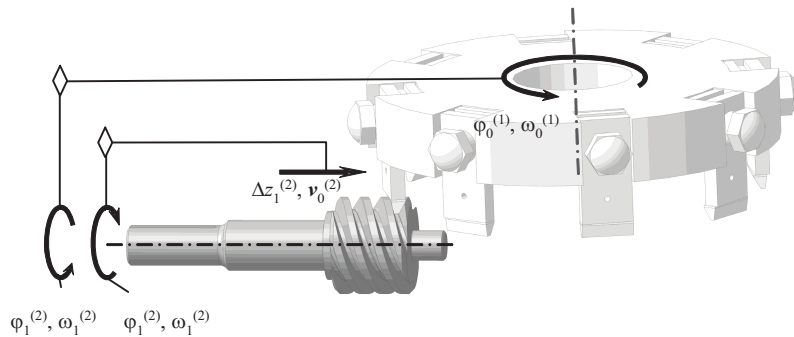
Формообразование витков многозаходного червяка производящей линией – режущей кромкой резца торцовой резцовой головки
